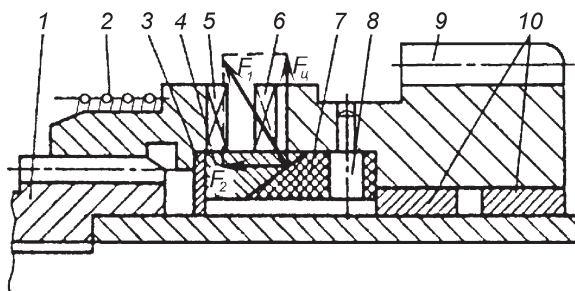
Центральный механизм храповичного привода и схема сил, действующих на его детали:
